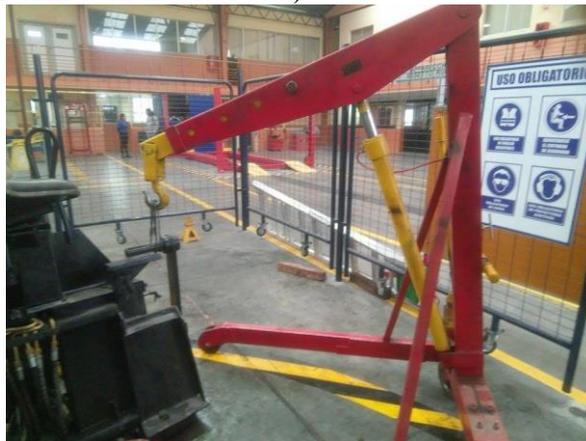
Pluma hidráulica elevando el estabilizador del aditamento. Fuente: Autores.
